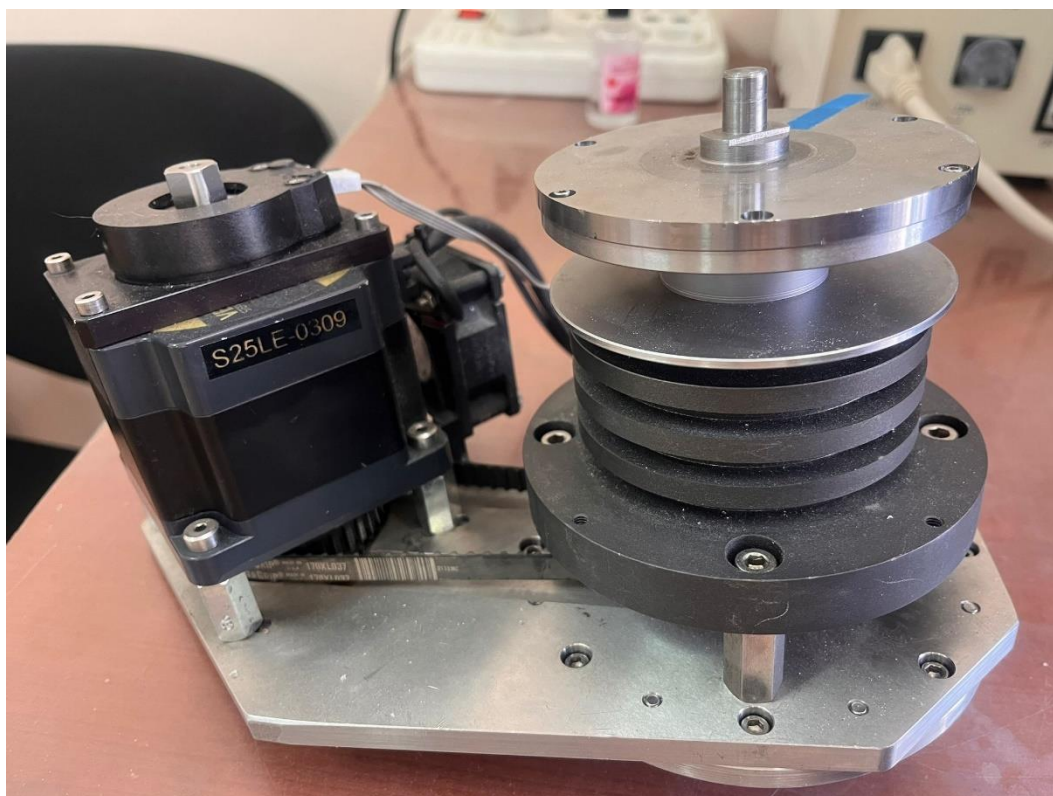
Modul S25LE-0309, masa rotativă
